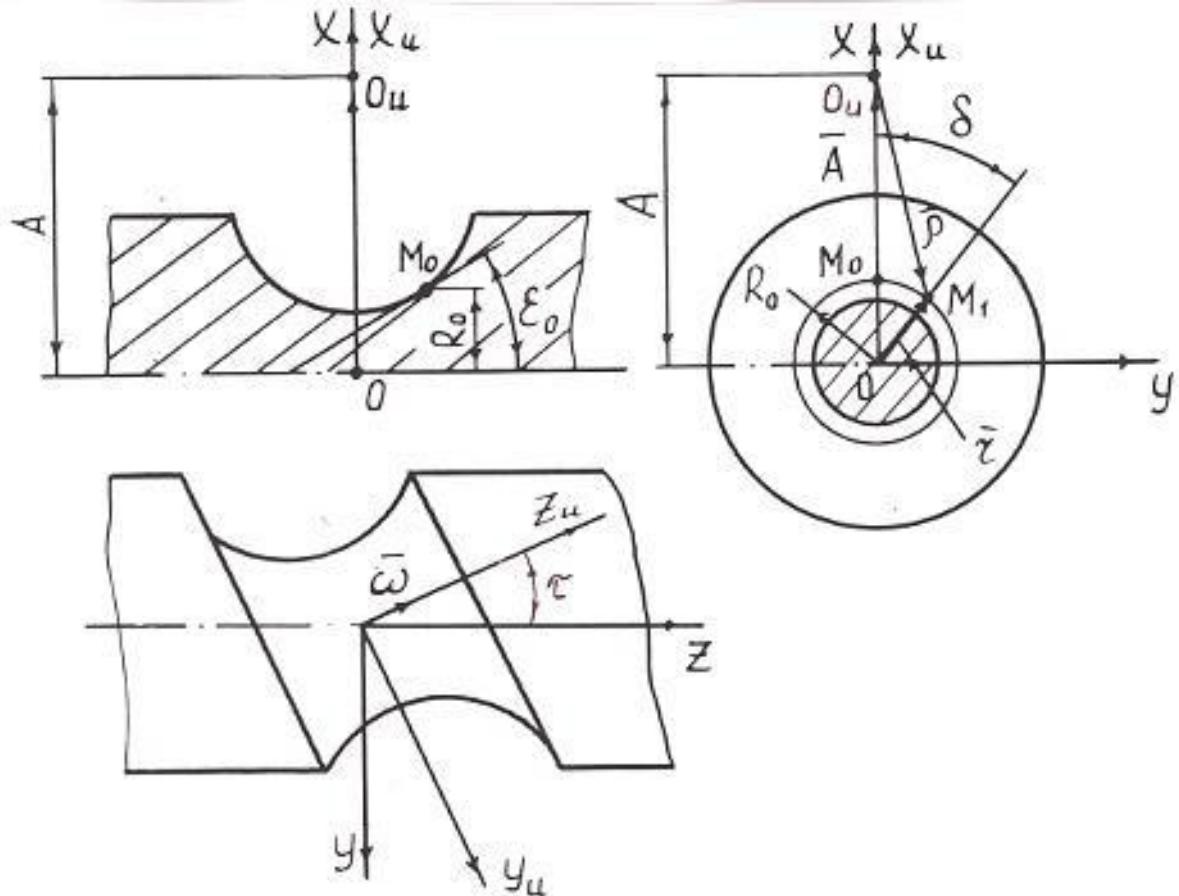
Профилирование дисковой фрезы для обработки винтовой поверхности
